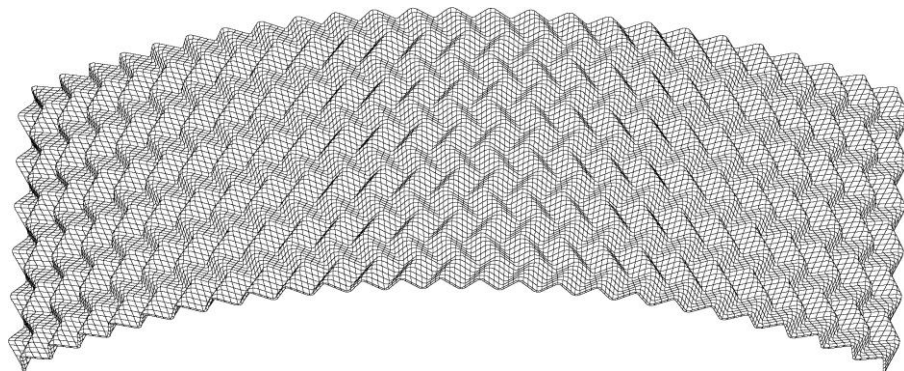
Зигзагообразный наполнитель СС для цилиндрической панели фюзеляжа.
